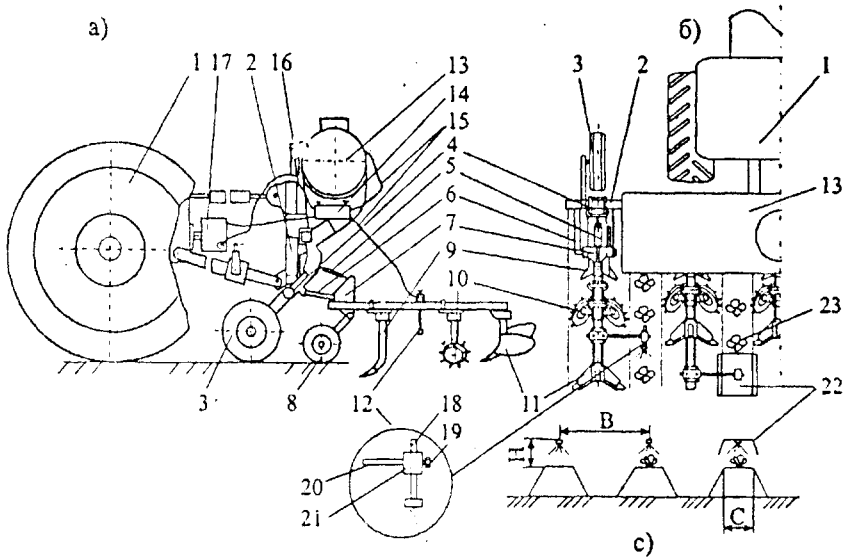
Агрегат для междурядной обработки и ленточного внесения гербицидов: а) вид сбоку; б) вид сверху; в) параметры обрабатываемой поверхности; 1- трактор; 2 - рама культиватора; 3 - колесо ходовое; 4 - кронштейн передний; 5- вит регулировочный; 6 - тяга; 7 - кронштейн задний; 8 - колесо опорное; 9 - стойка с рыхлительной лапой; 10 - борона роторная; 11 - корпус окучивающий; 12 - распыляющий рабочий орган; 13 - емкость для рабочего раствора; 14 - регулятор давления; 15 - всасывающая и нагнетательная коммуникация; 16 - фильтр; 17 - насос шестеренный; 18 - штанга вертикальная; 19 - фиксатор; 20 - штанга горизонтальная; 21 - втулка направляющая; 22 - устройство ветрозащитное; 23 - возделываемые растения
